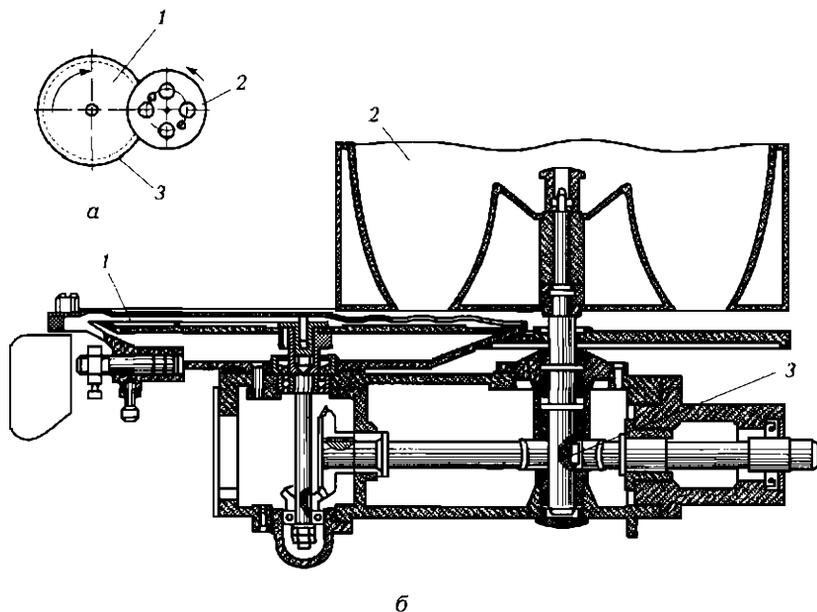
Сменный механизм для нарезания сырых овощей МС27-40: а — принцип работы нарезающего устройства; б — схема механизма. 1 — дисковый нож; 2 — загрузочный бункер; 3 — редуктор
